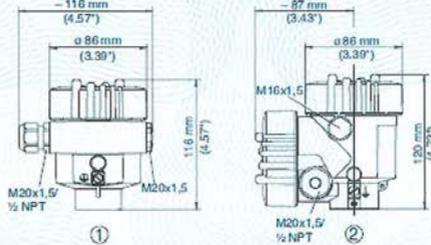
Алюмінієвий корпус (1 – однокамерний; 2 - двохкамерний)
